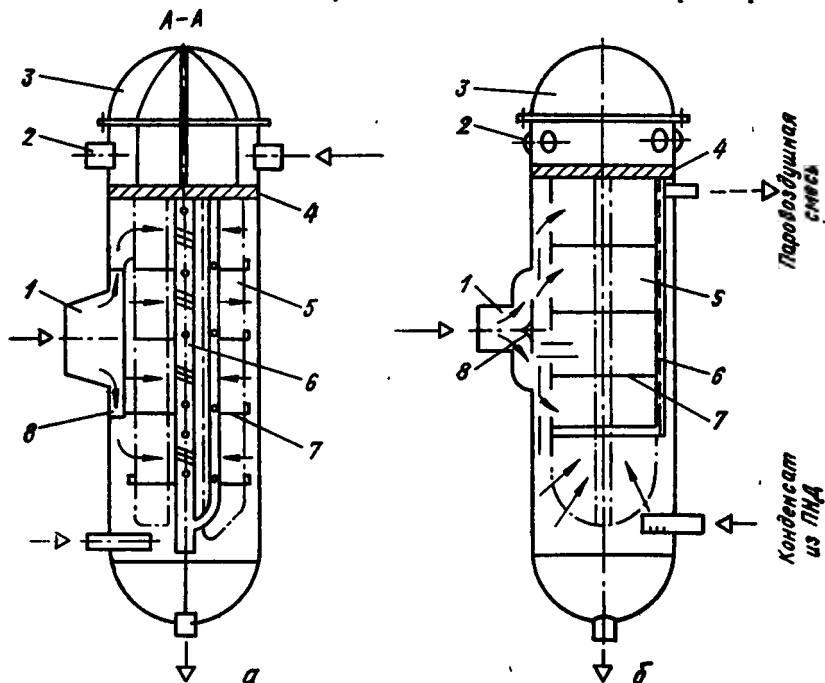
Схемы подогревателя низкого давления, работающего под вакуумом (а, б): 1 — патрубок подвода пара; 2 — патрубки питательной воды; 3 — крышка водяной камеры; 4 — трубная доска; 5 — трубный пучок; 6 — воздухоотсасывающая труба; 7 — промежуточная перегородка; 8 — паростойный щиток.
